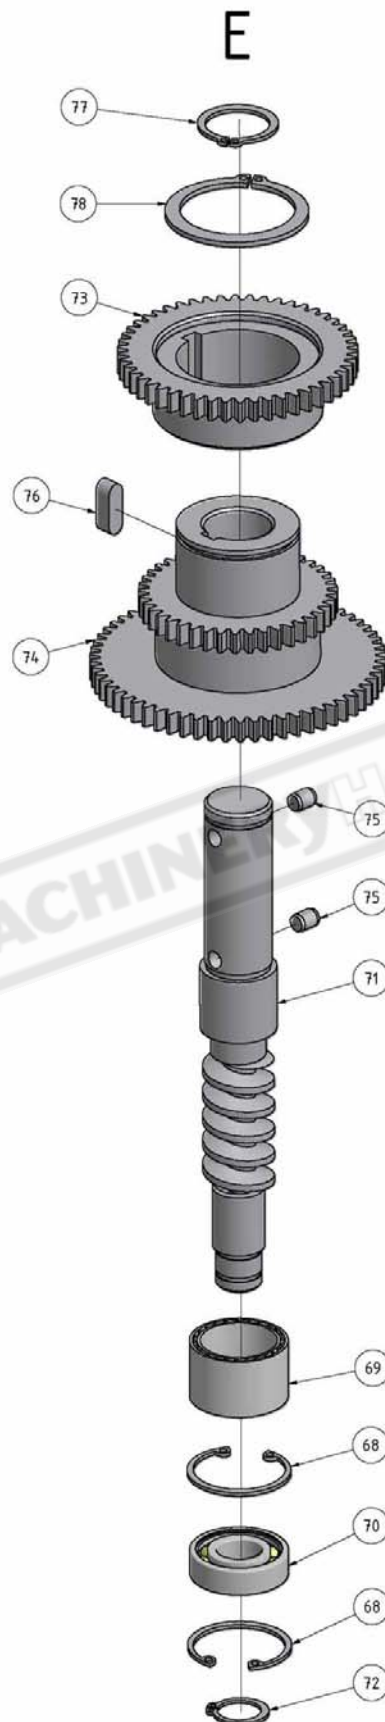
Bohrkopf 5 von 9 - Drilling head 5 of 9
